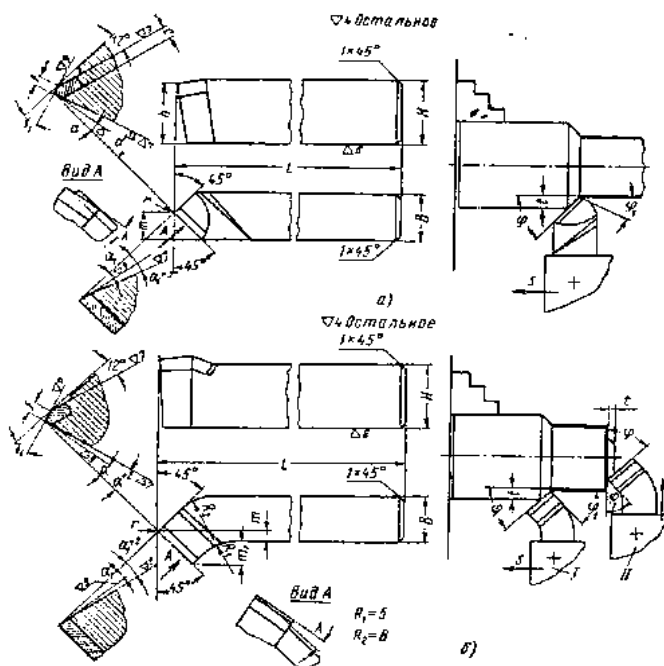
Токарные проходные резцы, оснащенные пластинками твердого сплава
